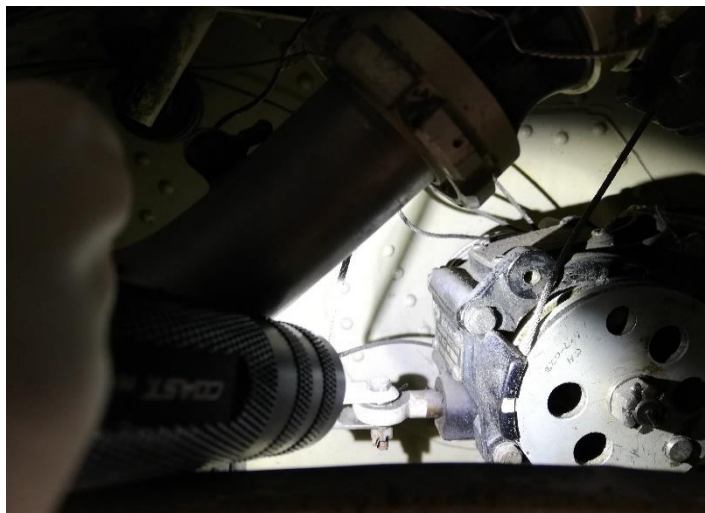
Limpieza e inspección de la compuerta izquierda del tren de aterrizaje
